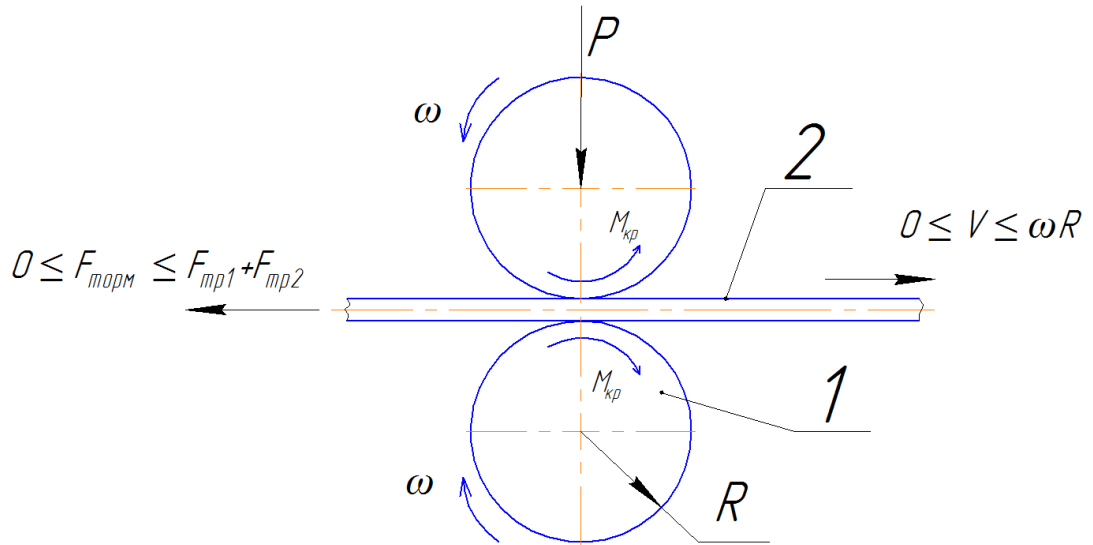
Схема приложения нагрузок к образцу: 1– валки; 2– образец
